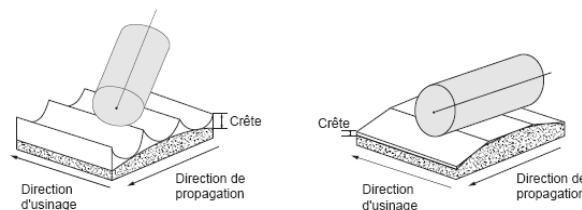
Usinage en bout et en flanc [Takeuchi et al 1995]
